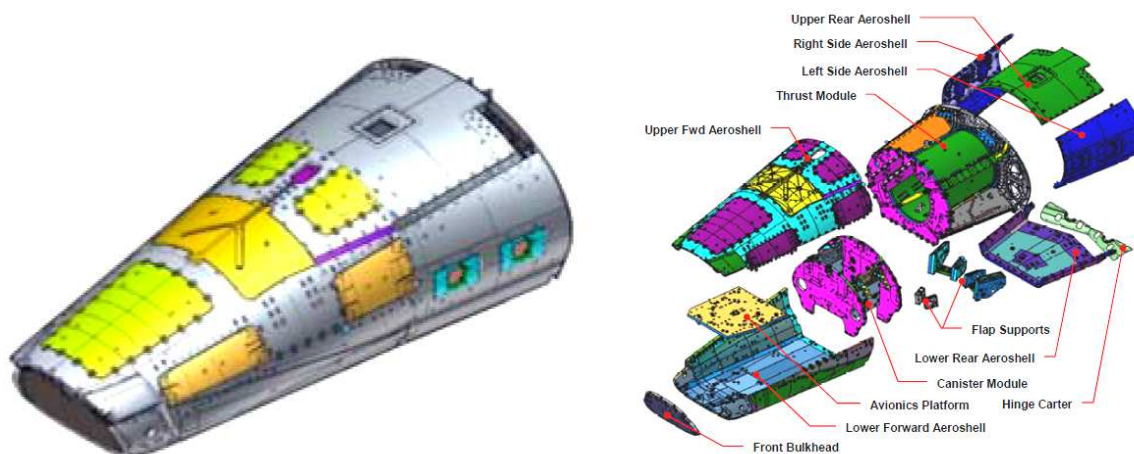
Конструкция корпуса ВА НК в сборе⁴
